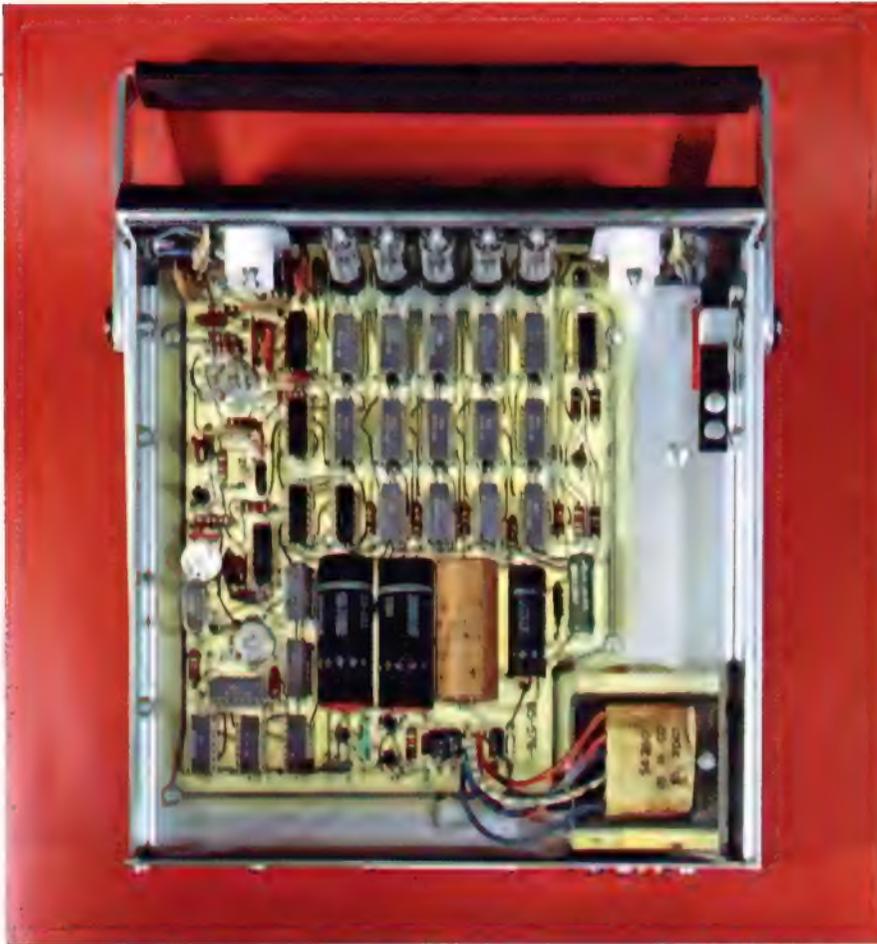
Innenansicht des kompakt aufgebauten Gerätes
